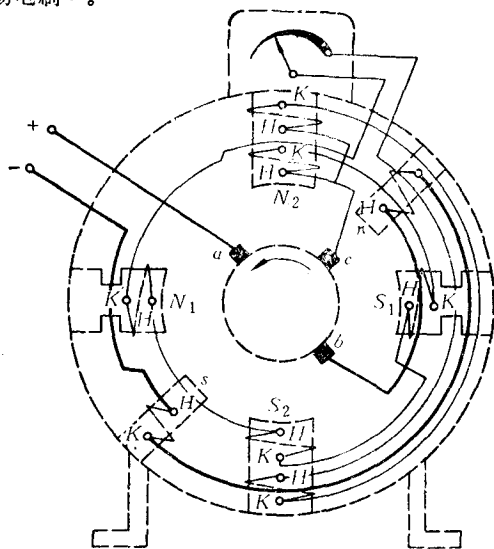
AX-320型焊接发电机内部接线图(自换向器端视图)
